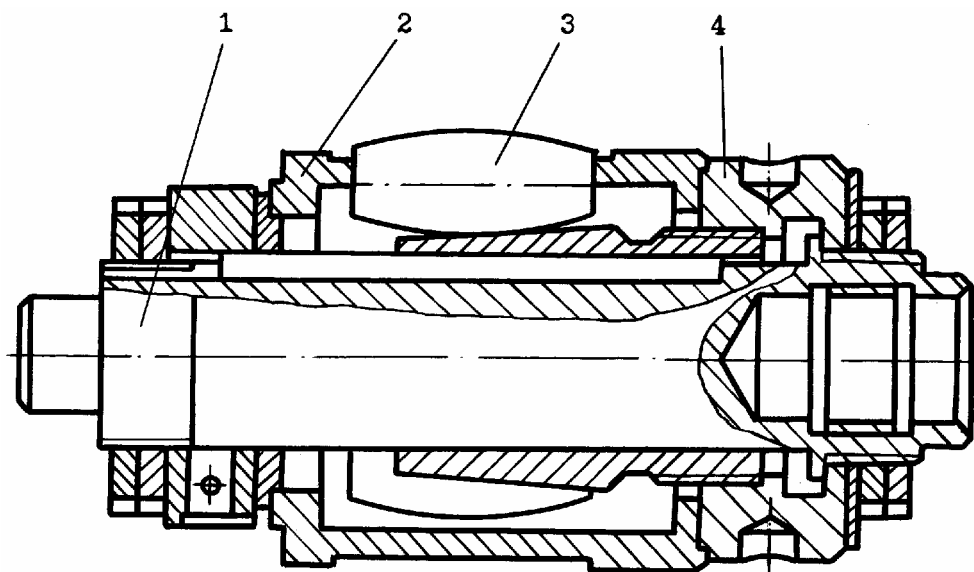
Устройство для раскатывания отверстий: 1 – вал; 2 – корпус; 3 – ролик; 4 – гайка
